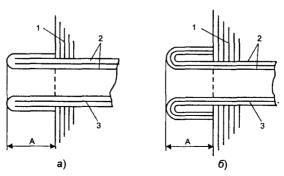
Расположение пазовой коробочки в пазу и вылет манжеты: a — манжета, образованная внутренним слоем пазовой коробочки, b — манжета, образованная тремя слоями пазовой коробочки; b — пакет железа, b — электрокартон, b — внутренний слой лакоткани или миканита
